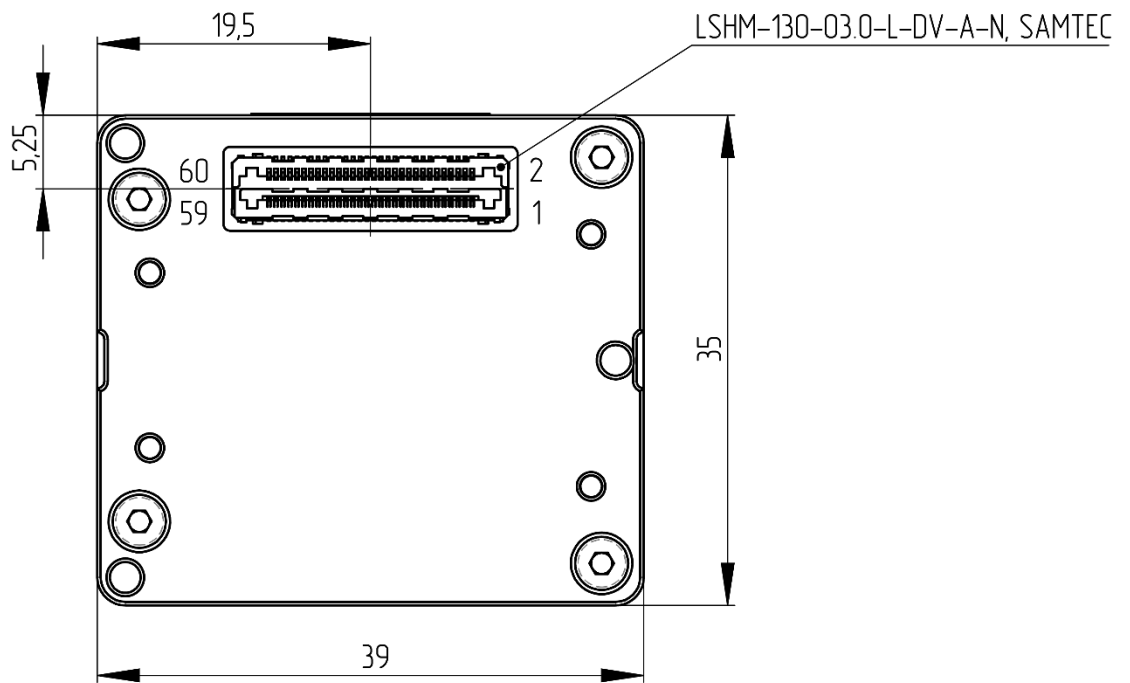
Габаритный чертеж ГKB-3 ВМ
